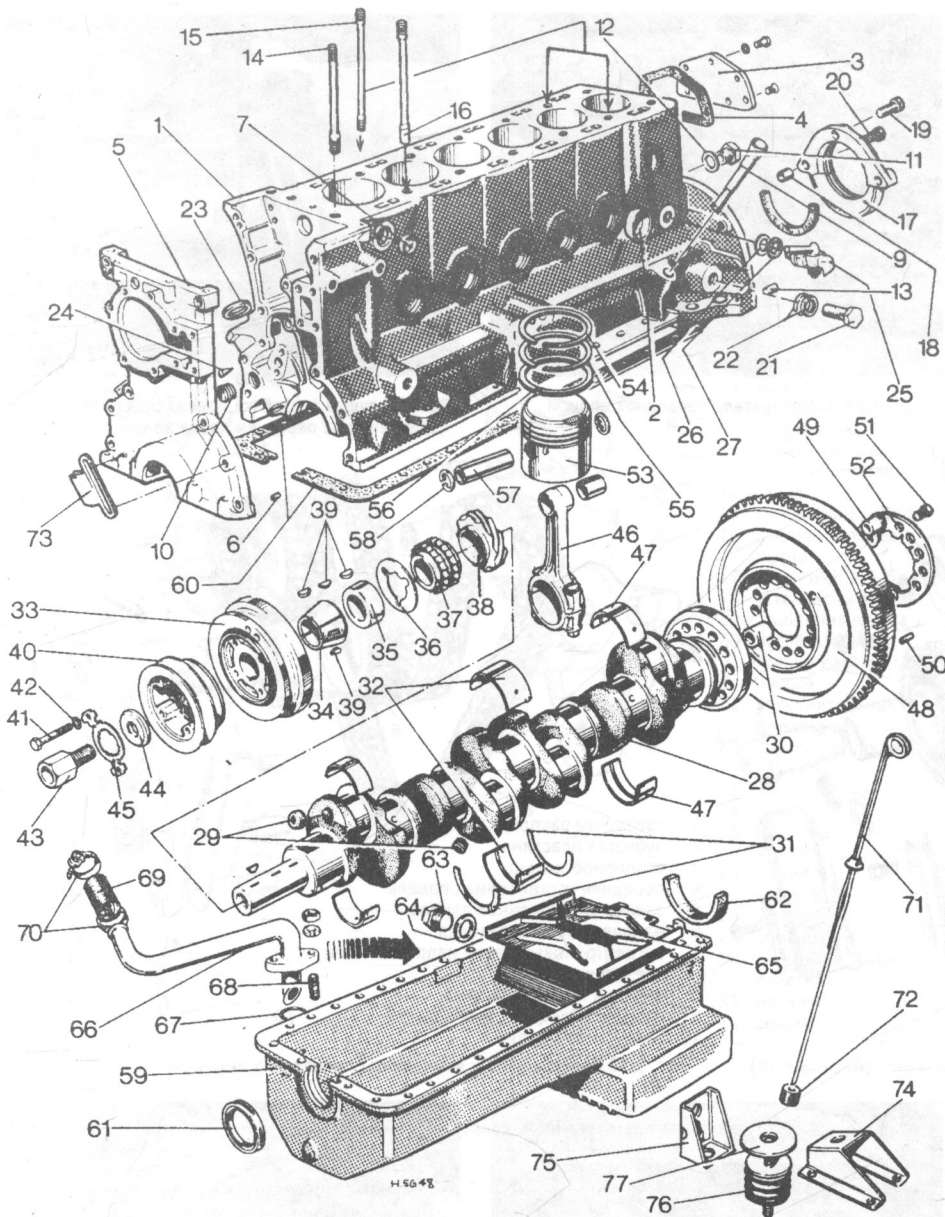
Компоненты коленчатого вала и блока цилиндров
